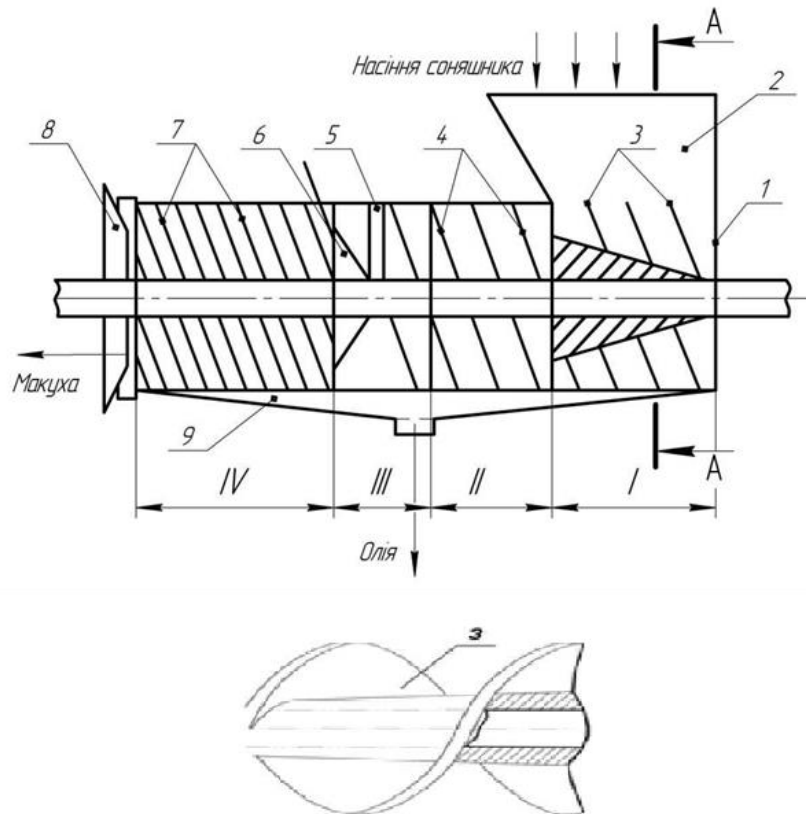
Конструктивно-технологічна схема шнекового пресу для віджиму олії з насіння соняшника: 1 - корпус; 2 - завантажувальний бункер; 3 - подавальний шнек; 4 - пресувальний шнек; 5 розпушувач мезги; 6 - конусна втулка; 7 - шнек зі зменшеним кроком витка; 8- регулятор тиску; 9 – піддон для відведення олії.
